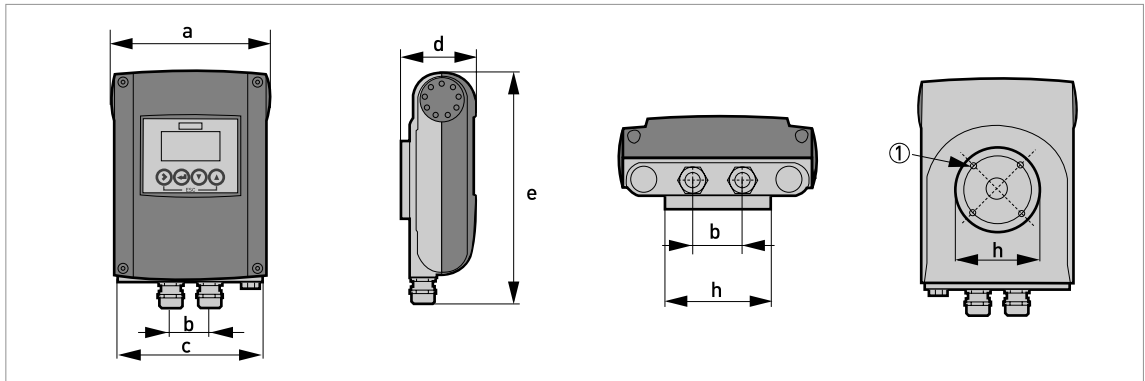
Abmessungen für Kompaktausführung (0°), Aluminiumgehäuse
